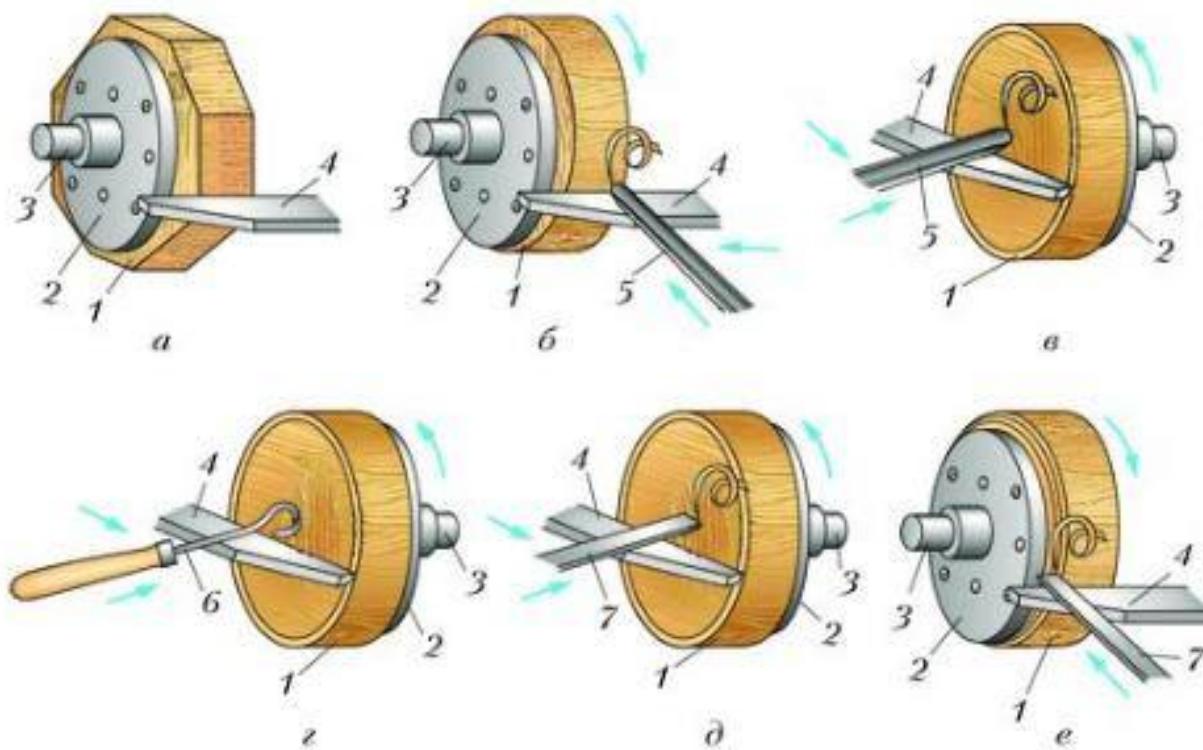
Технология изготовления вазы: а – установка заготовки на станок; б – черновое точение; в – обработка внутренней полости рейером; г – обработка полости крючком; д – зачистка донышка; е – подрезание основания; 1 – заготовка; 2 – планшайба; 3 – шинидель станка; 4 – подручник; 5 – полукруглая стамеска; 6 – крючок; 7 – плоская стамеска
